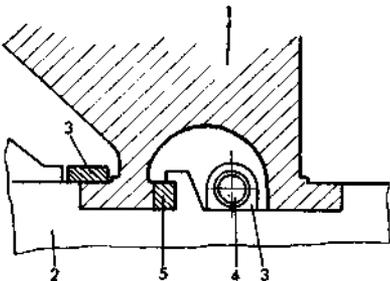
Situación de los husillos de elevación de la traviesa. Vista por A de la -figura 332.
